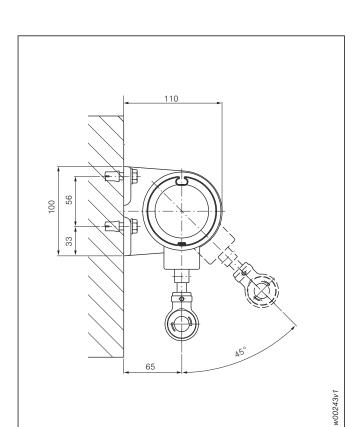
Wandmontage mit außenliegendem Kurbelantrieb
